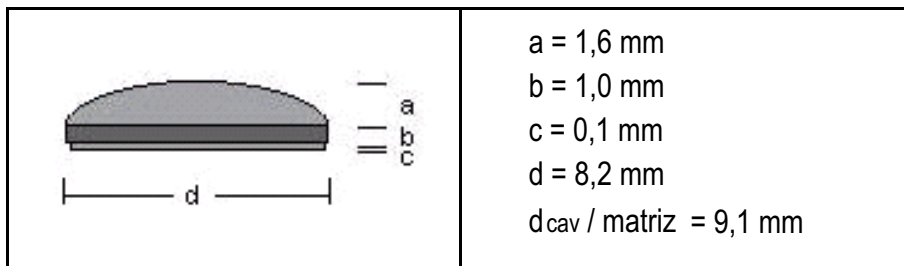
Desenho dimensional do ímã para palmilha pequena.
